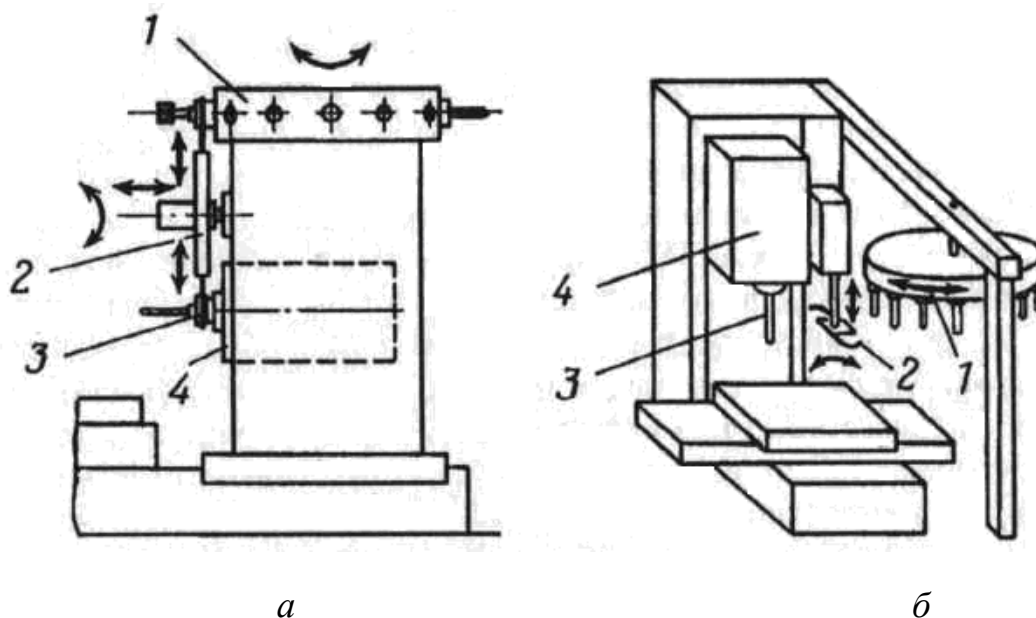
Пристрої автоматичної зміни інструмента з автооператорами: а – для верстатів з горизонтальною віссю шпинделя; б – для верстатів з вертикальною віссю шпинделя
